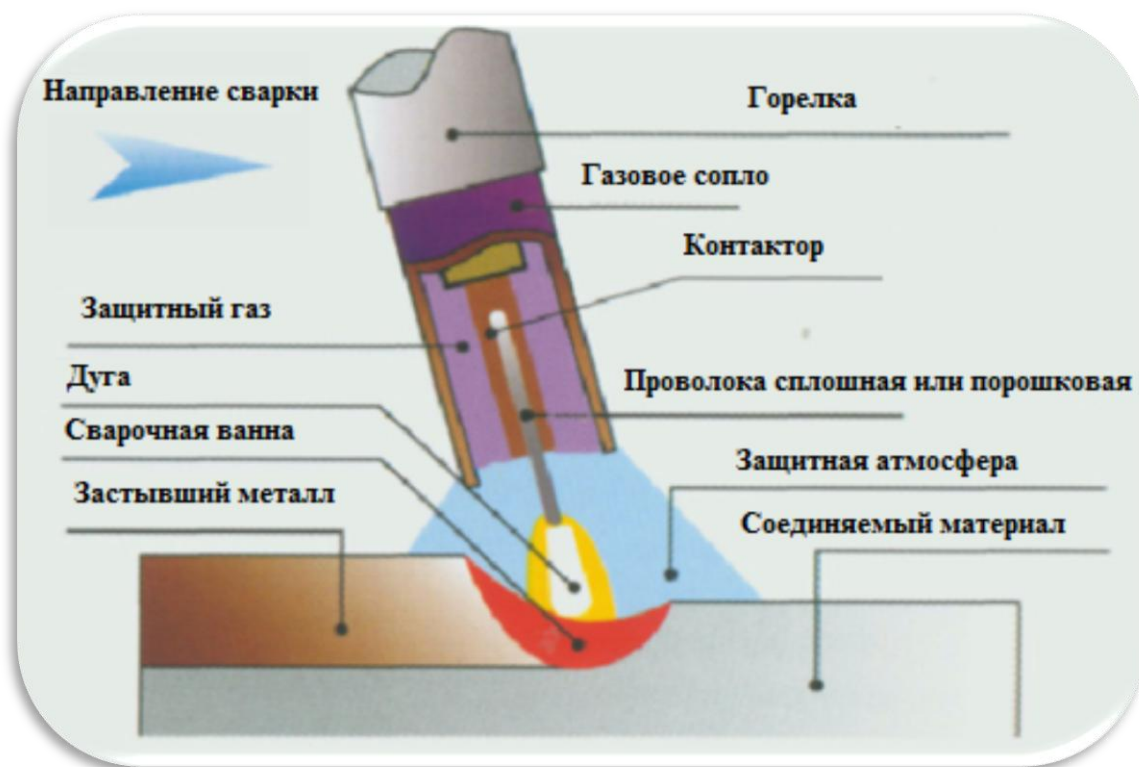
Процесс сварки в среде углекислого газа.
